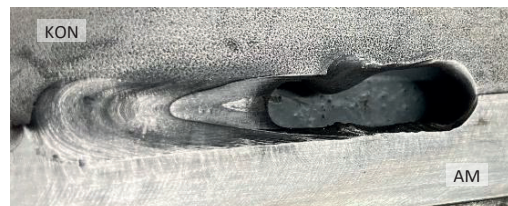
Durchbrand bei hybrider WIG-Schweißnaht, additiv gefertigtes Blech mittels DED-Arc (MSG), AISI 316L.
